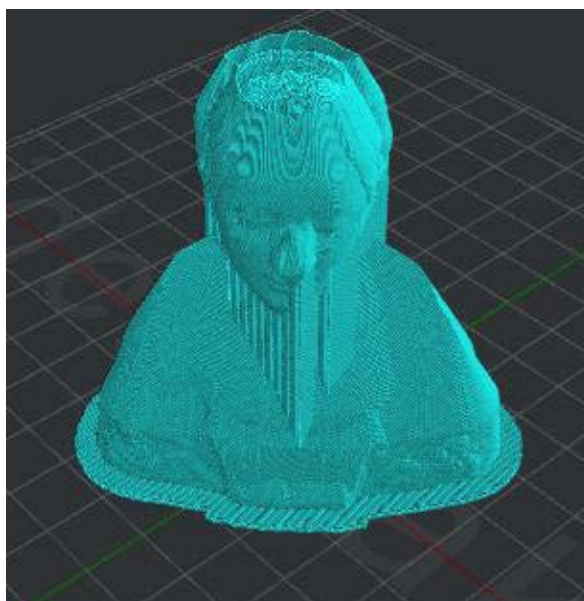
Nastavnení dvou stěn otírací zdi.
